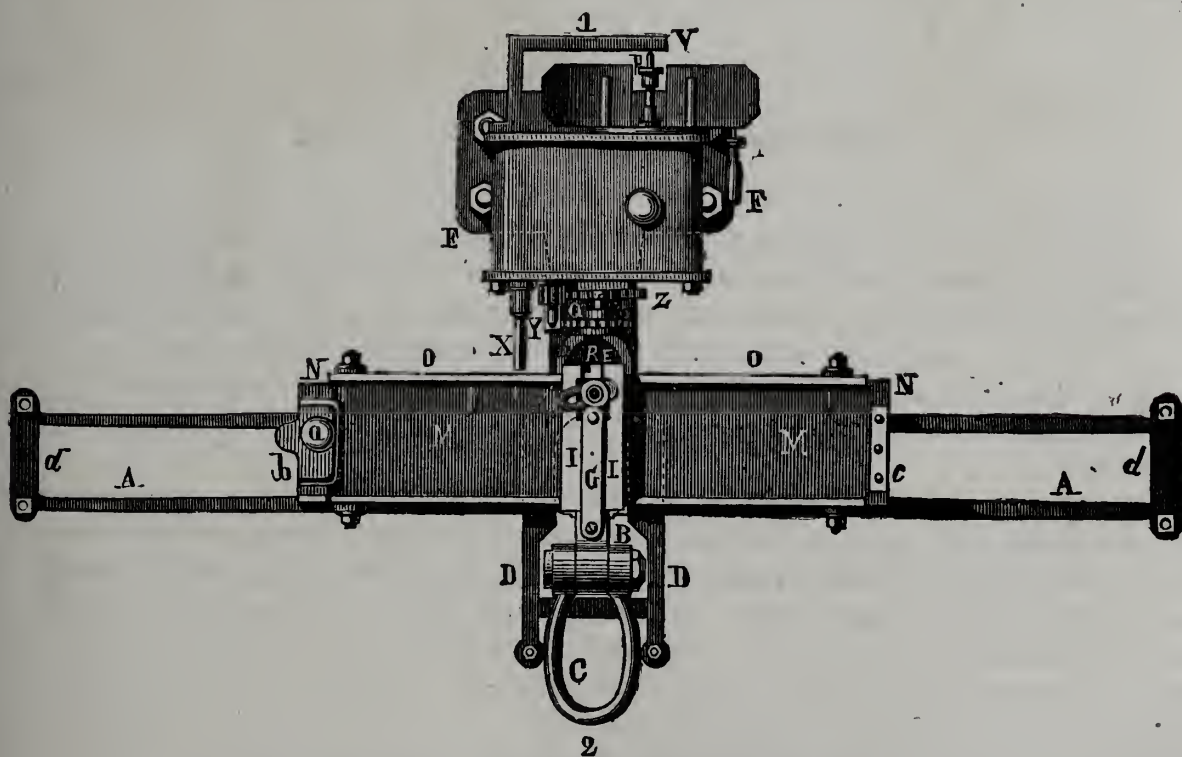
Plan d'un dynamomètre-graveur, construit par M. A. Clair.
